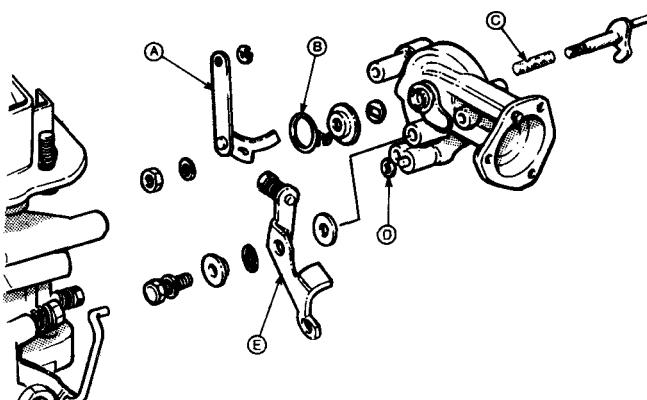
Узел автоматической воздушной заслонки - карбюратор WEBER. А - Верхний рычаг заслонки. В - Пружина. С - Втулка. Д - Уплотнительное кольцо. Е - Передаточный рычаг и регулировочный винт.
